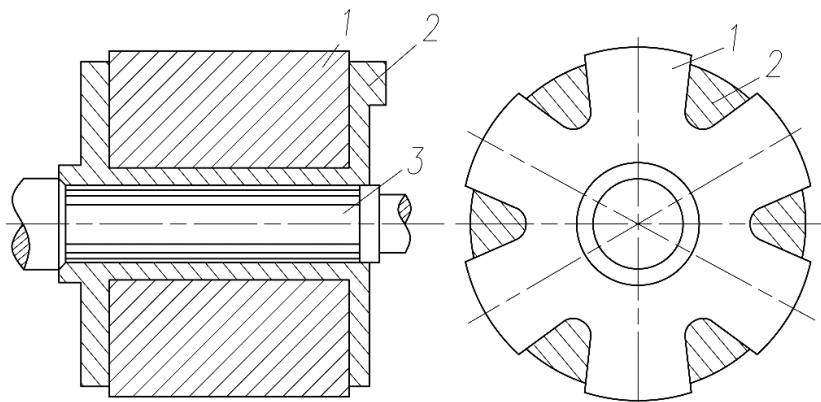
Общий вид ротора с явнополюсной магнитной системой: 1 — железо ротора; 2 — магнитная заливка; 3 — вал.
